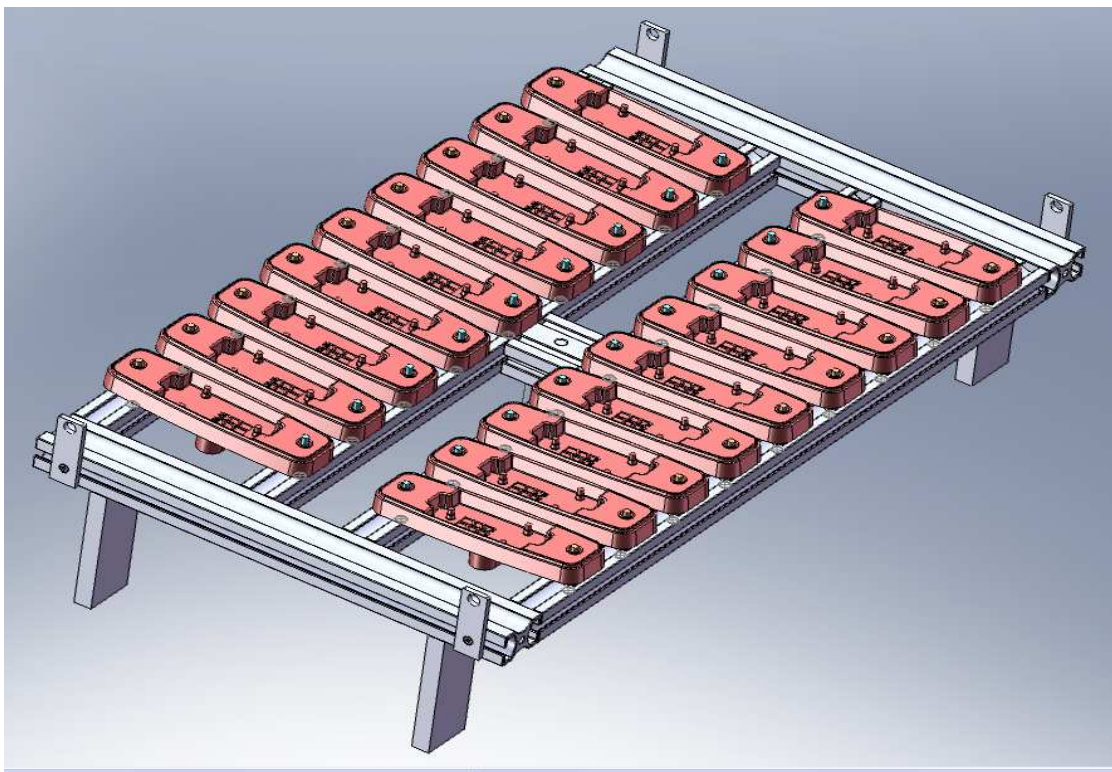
Assembly Suporte 90° B Sidemarker Zeta
